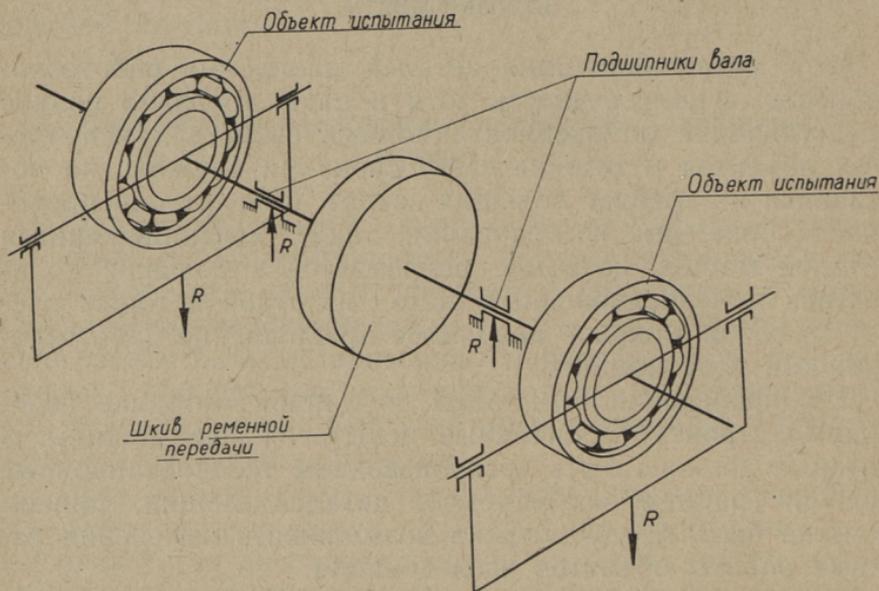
Схема станка для испытания шарикоподшипников на долговечность.
